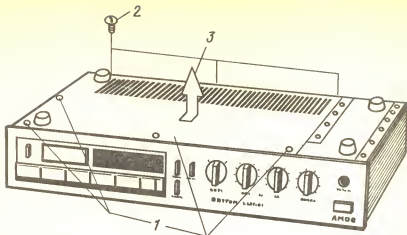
Снятие нижней крышки корпуса (цифрами указаны порядок разборки):
